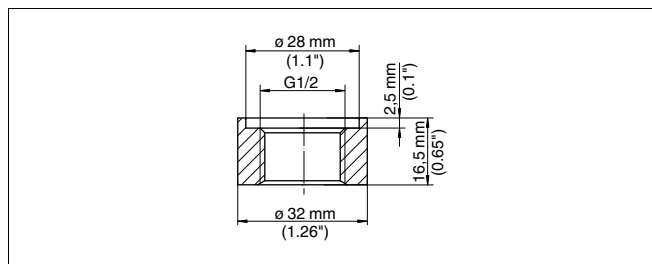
Medidas racor soldado G $\frac{1}{2}$  A según DIN 3852-X
